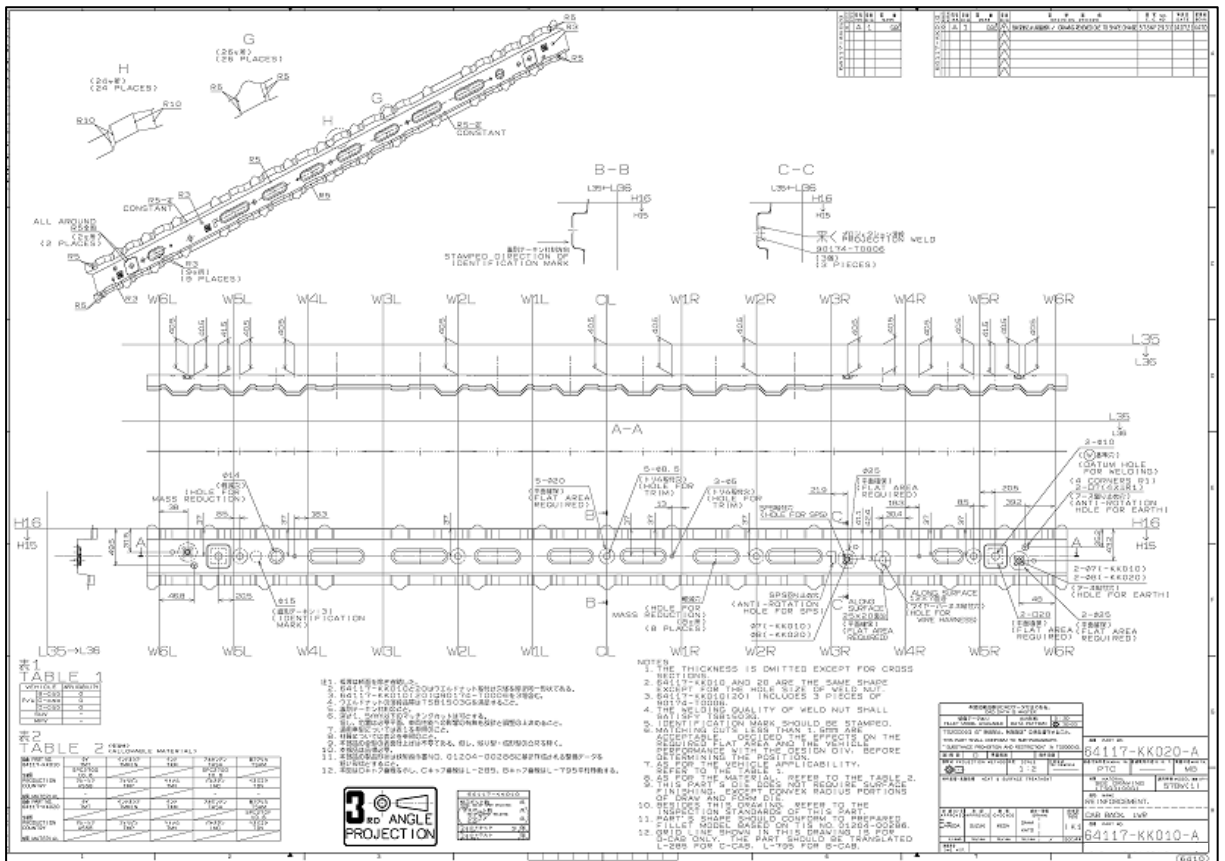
Plano de Diseño de un subconjunto estampado con tuercas soldadas por proyección.
